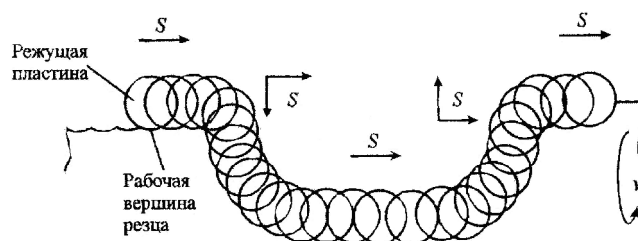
Схема обработки ручья прокатного валка резов с круглой режущей пластиной.
